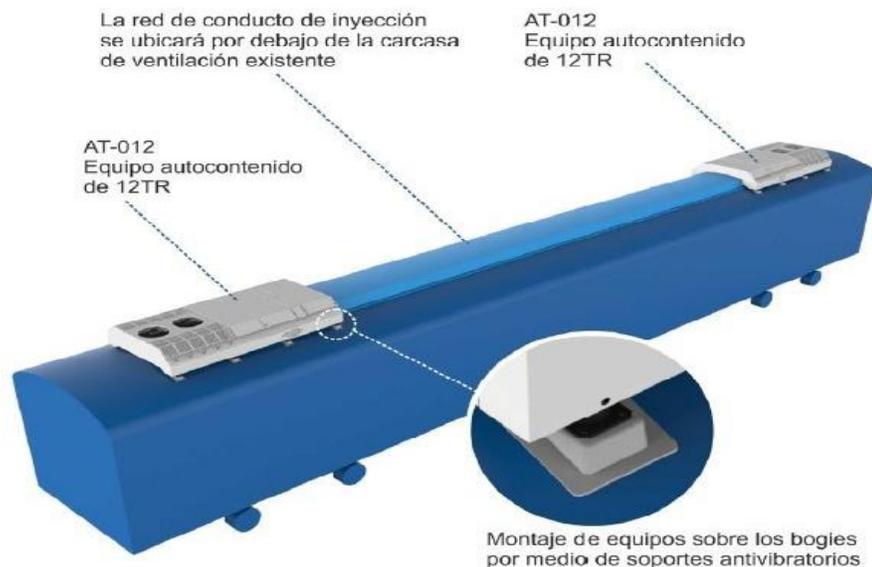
Montaje de equipos de aire acondicionado sobre techo de coche.
